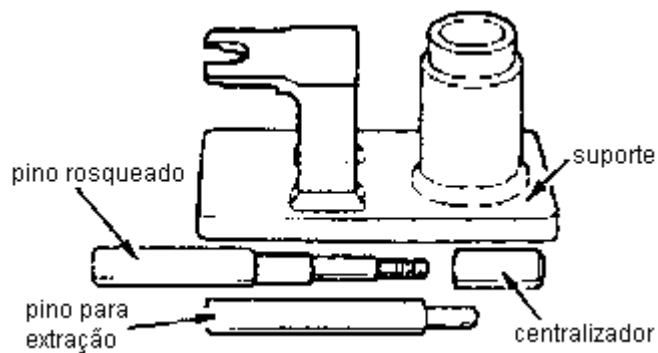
Ferramenta para desmontagem e montagem do pino do êmbolo.
